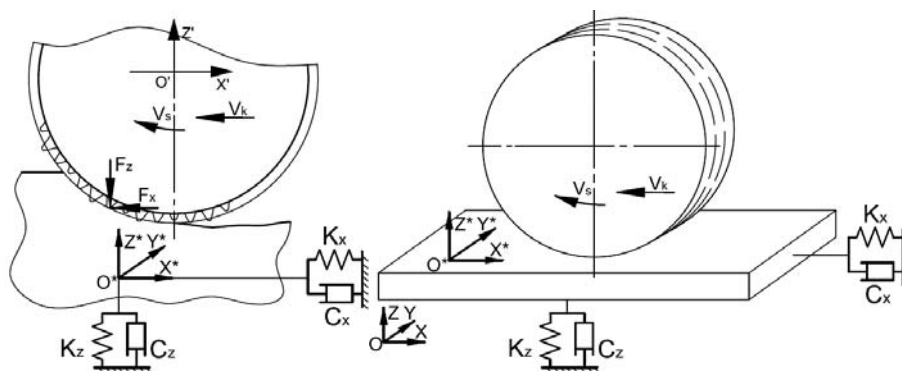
Динамічна схема моделювання обробки поверхні при шліфуванні з урахуванням податливості деталі.
